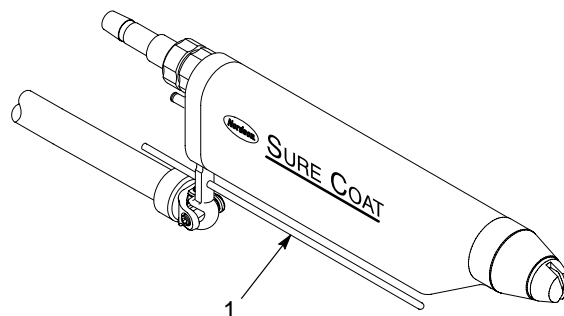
Kit de colector de iões para pistola com barra de suporte
